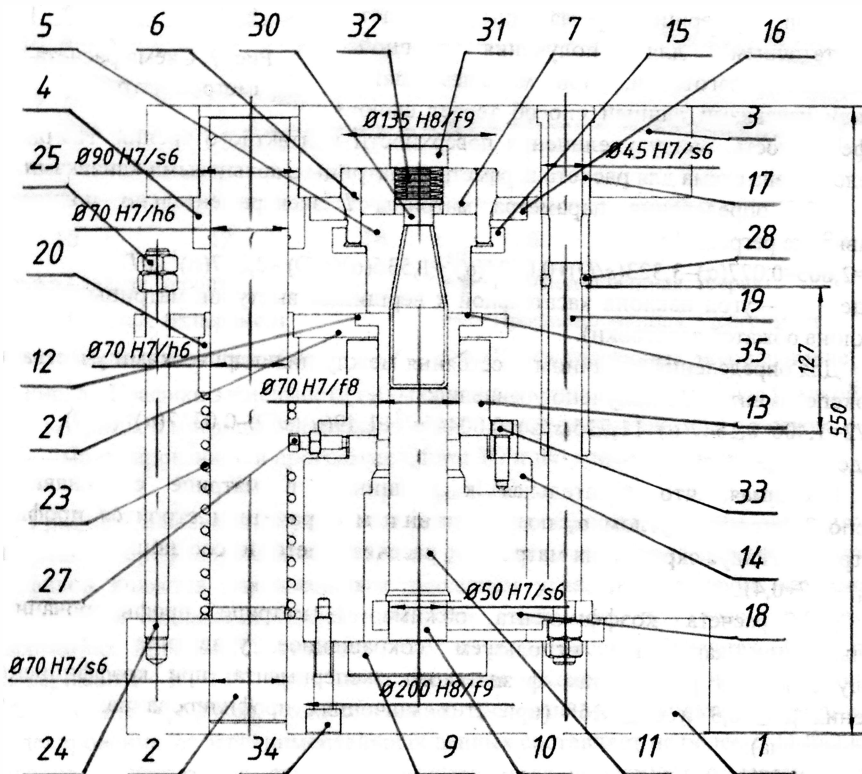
Штамп с плавающей оправкой и матрицей с кольцевыми канавками
